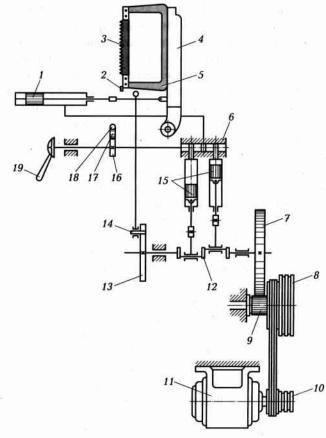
Кинематическая схема отрезного ножовочного станка:
